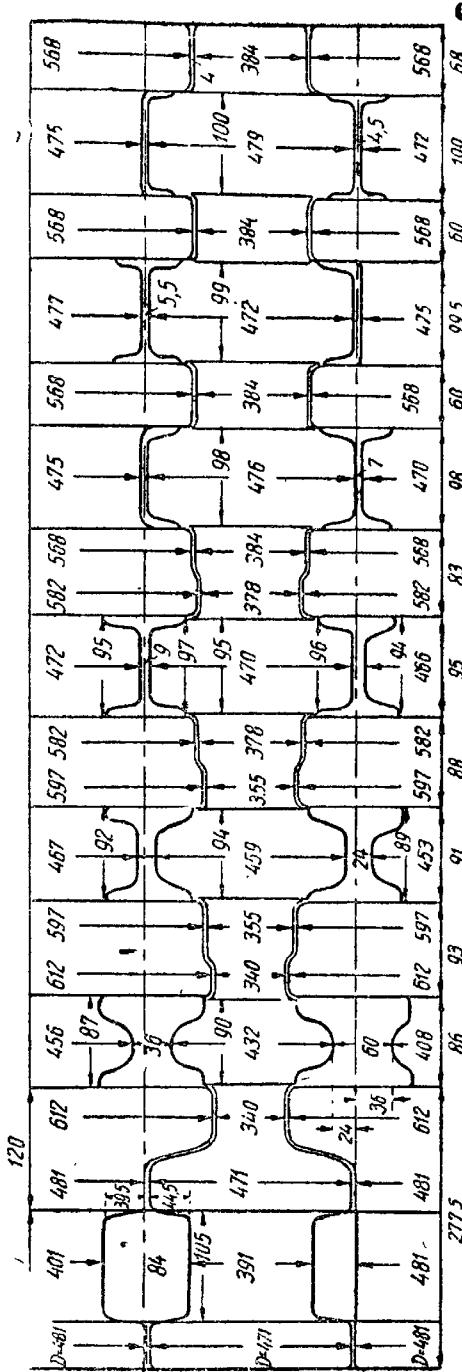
Калибровка двухтавровой балки № 10—100 × 57 × 4,5. Расположение ручьев в валках.
